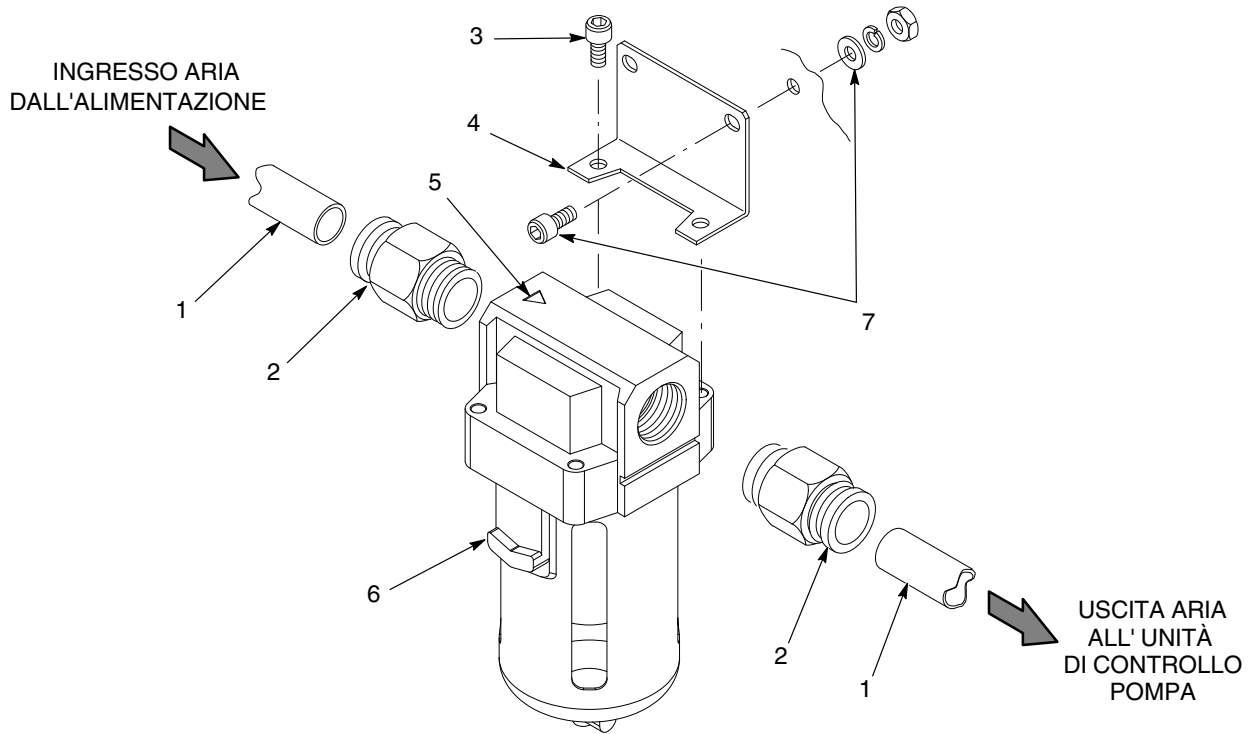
Installazione del filtro dell'aria - Sistemi autonomi e con montaggio su rotaia/parete
